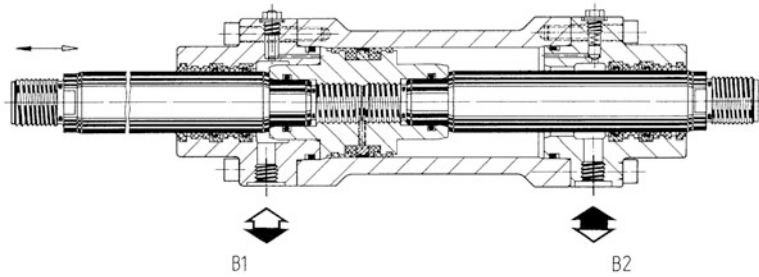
Gleichlauf- oder Zweistangenzylinder in Rundbauform, Mehrschraubenverbindung mit Integralfansch (HHN 812, schwere Ausführung, Hunger Hydraulik), Gleitring-Kompakt-Kolbendichtung mit integrierter Führung (Gleitring-Dichtsatz GD 1000 K), Tandem-Gleitring-Kompakt-Stangendichtungen (Tandem-Dichtsatz TDI) mit Führungsringen
